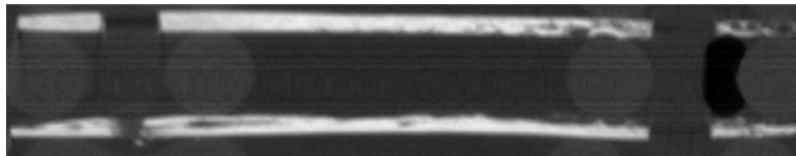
Reconstrucción digital del alzado de las muestras 48_12 y 35_12.
